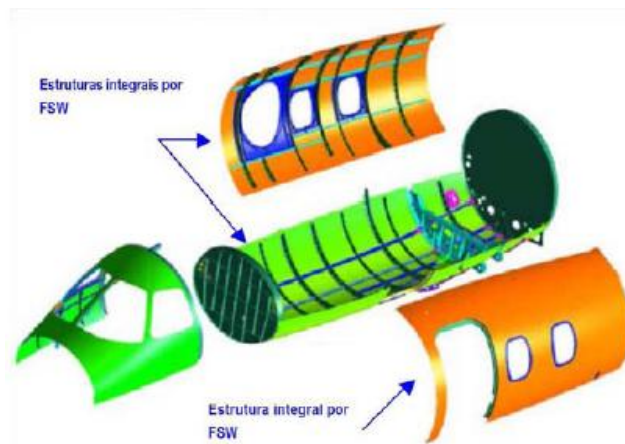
Soldadura realizada por FSW para aeronave Eclipse 500 [11]
